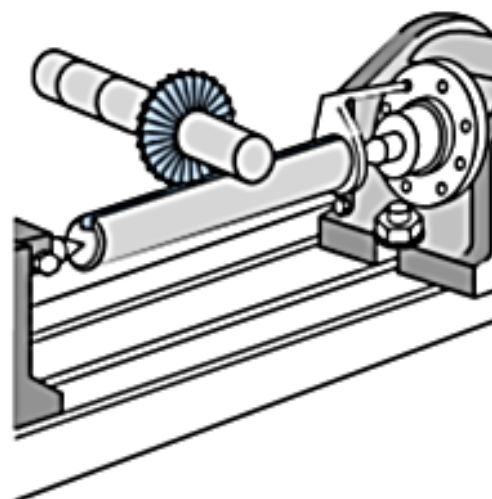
Установка фрезы при фрезеровании прямых канавок и шлицов
